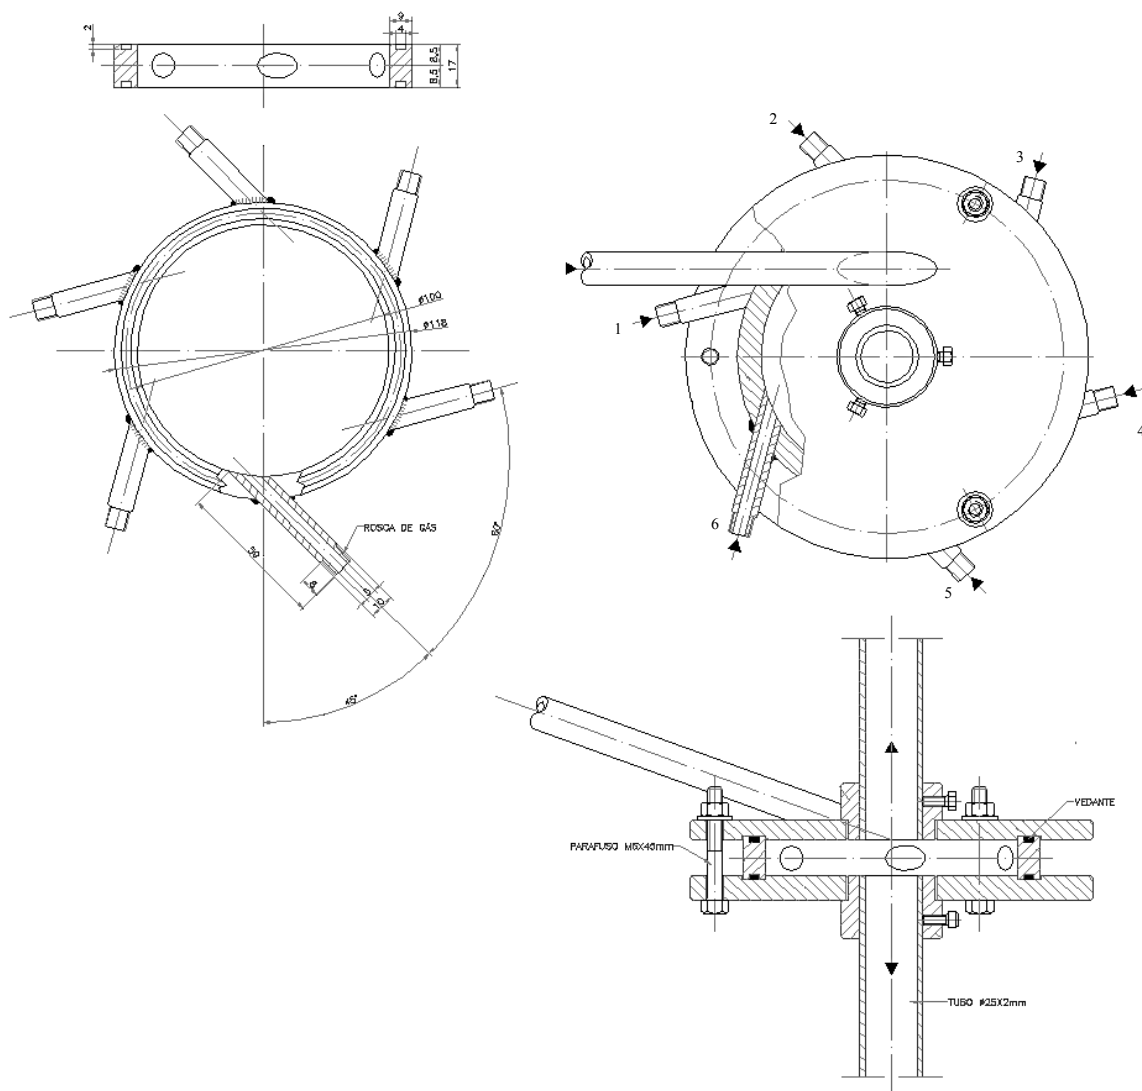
Desenho de projectivo construtivo do *jet mill* (com tubo de injeção de material).
